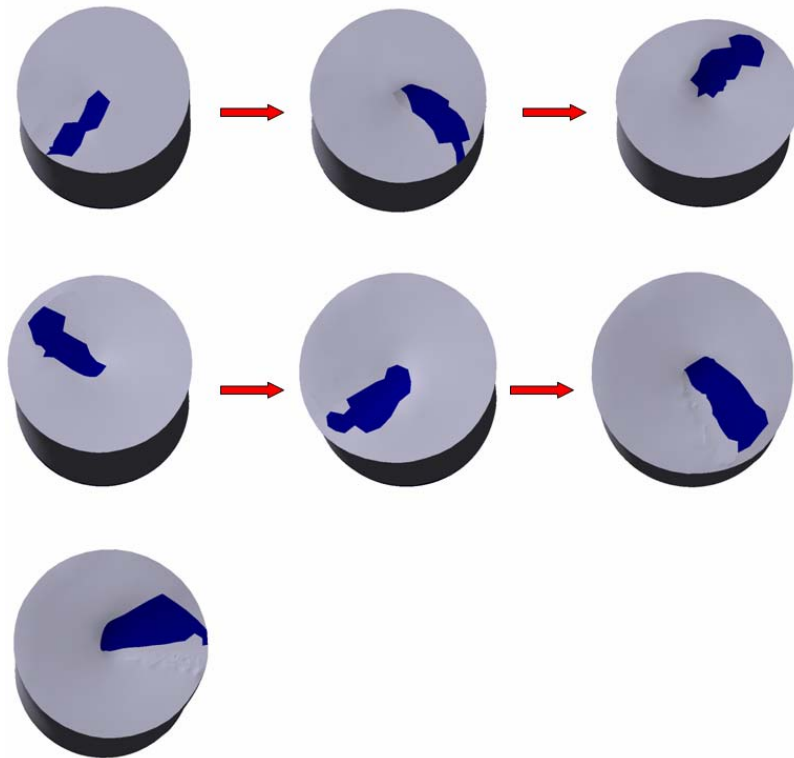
Изменение контура пятна контакта на верхней торцевой поверхности заготовки
